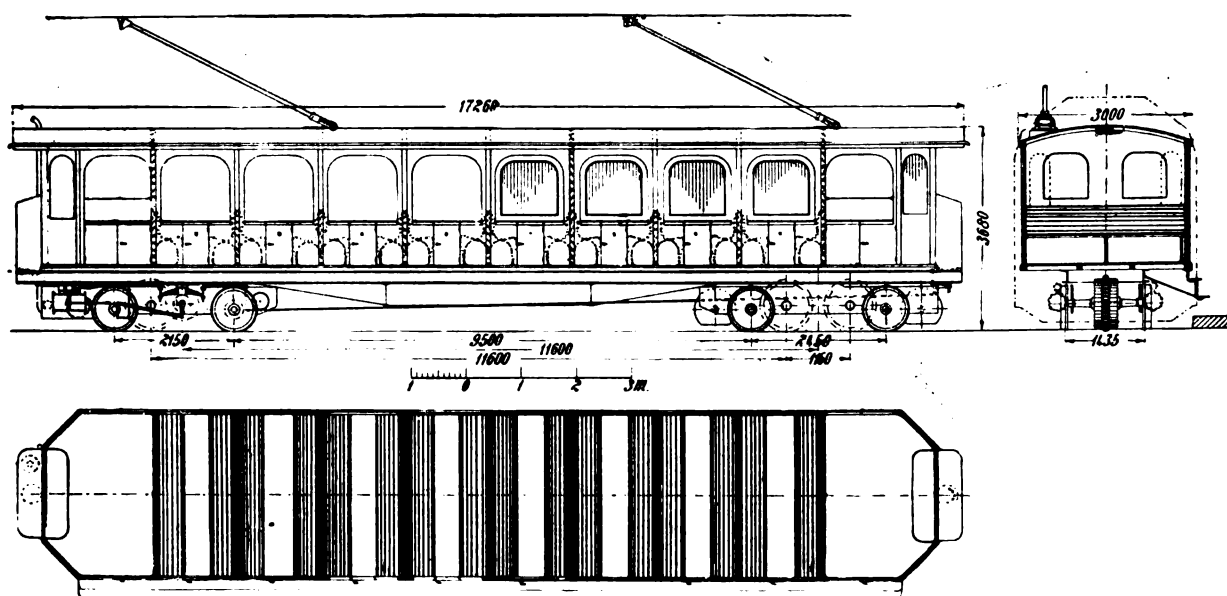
, 23 e 24. — Vetture della ferrovia del Righi. - Elevazione, sezione e pianta
